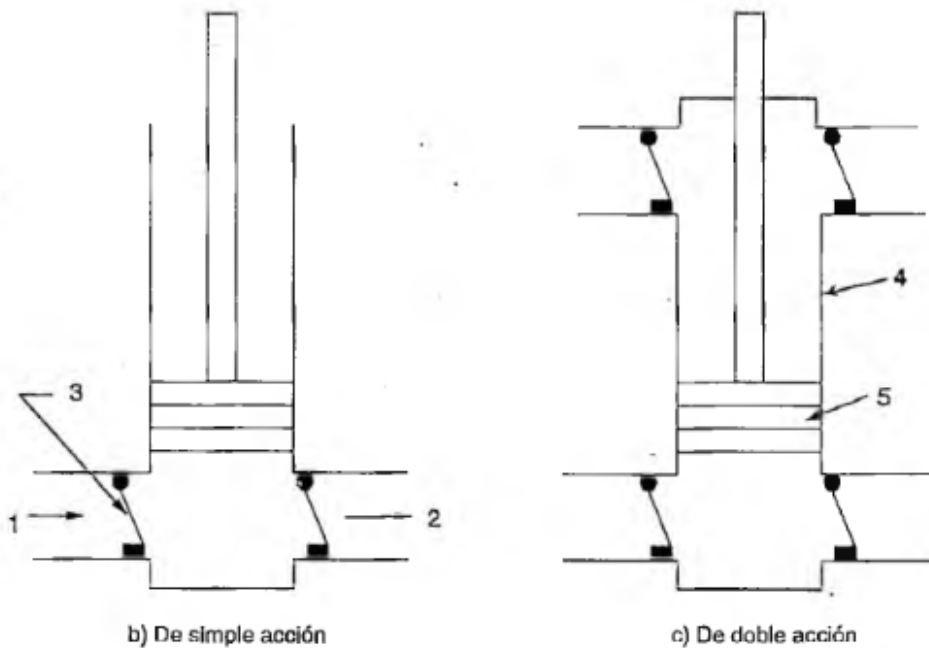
b) De simple acción; c) de doble acción: 1. Admisión, 2. Descarga, 3. Válvulas de placa, 4. Bloque del cilindro, 5. Pistón.
